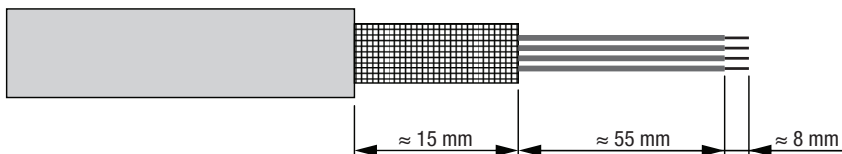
Confección del cable para la cubierta de bornes MK 308
